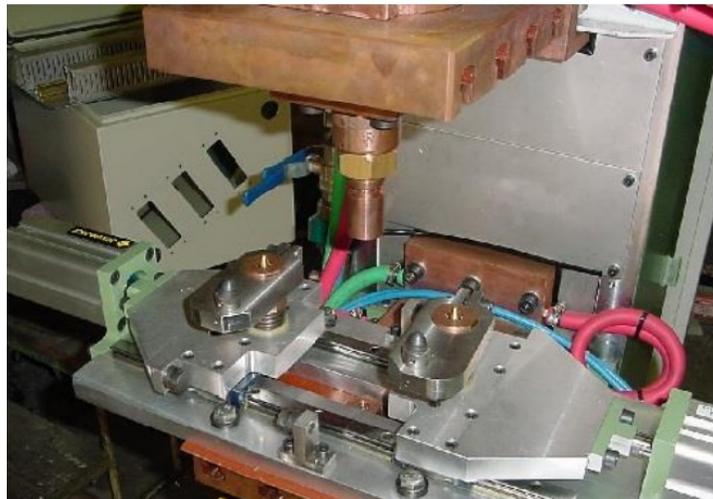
Máquina tipo prensa para soldar por proyección.
